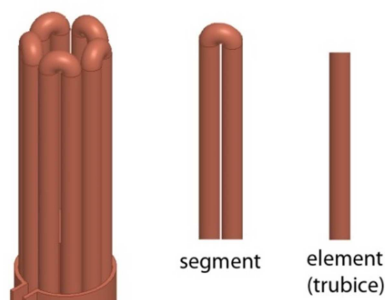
Kelímek s integrovaným induktorem [22]
